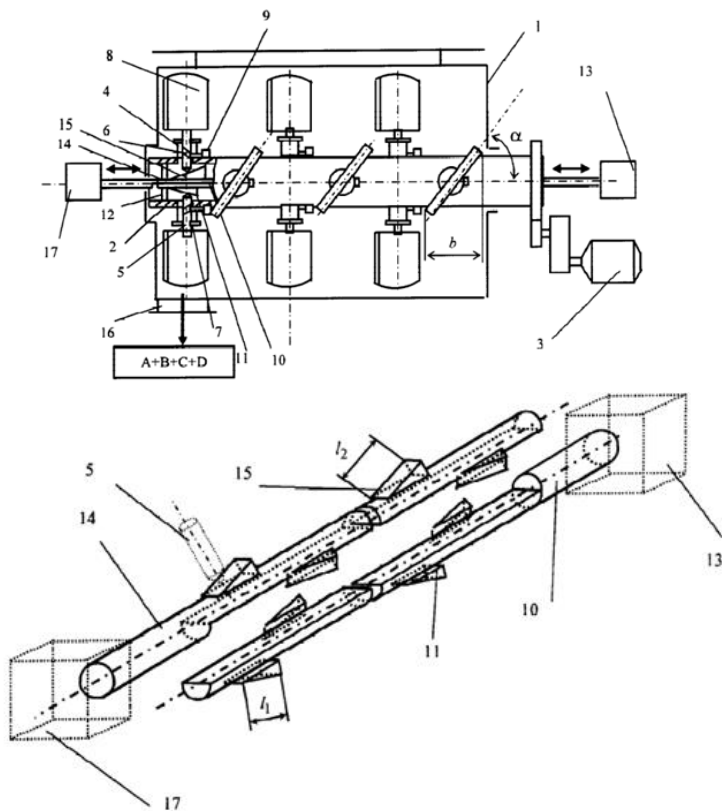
Вид ротора с устройством поворота лопастей. 1-корпус; 2-вал; 3-привод; 4-ось; 6-канавка; 7-уплотнение; 8-лопасть; 9-штифт; 10, 14-штанга; 11, 15-упор; 12-уплотнение; 13, 17-реверсивный механизм; 16-патрубок.
